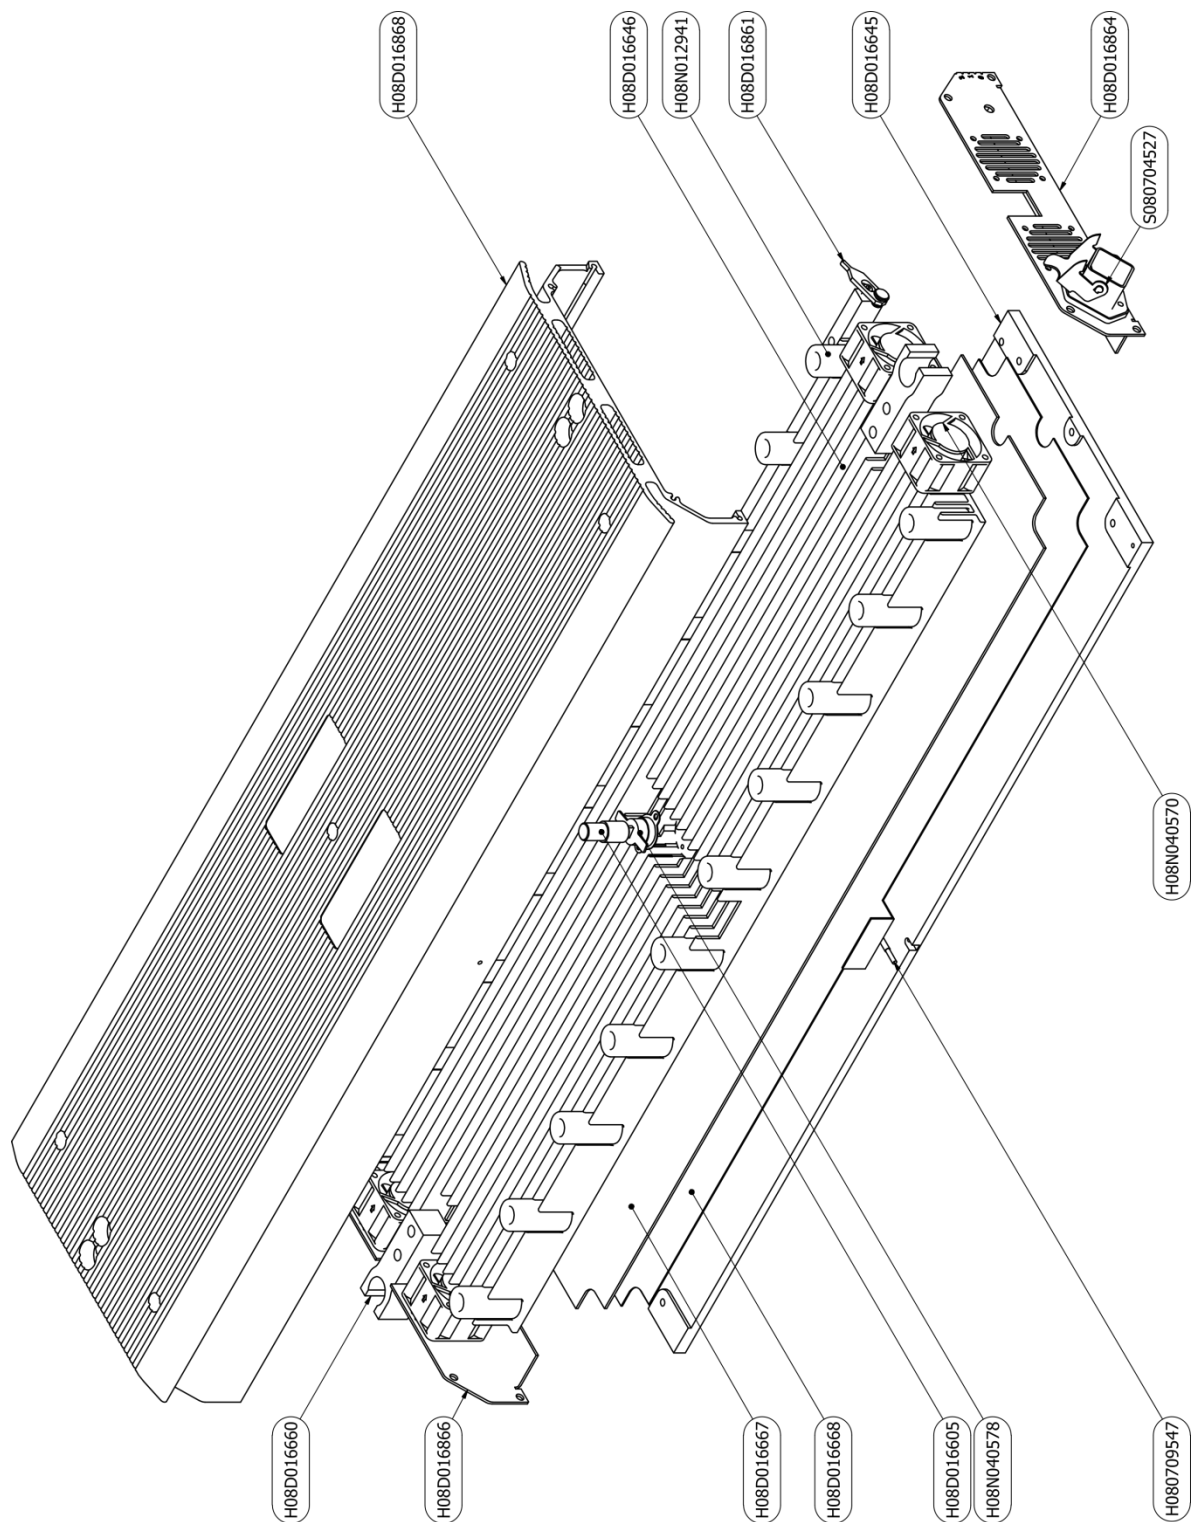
H08D016644 Unidad de placa de calentamiento superior PML-600
